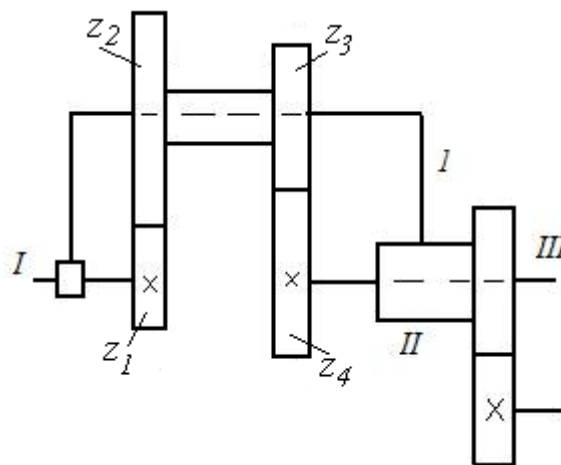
Дифференциальный механизм с цилиндрическими зубчатыми колесами.
